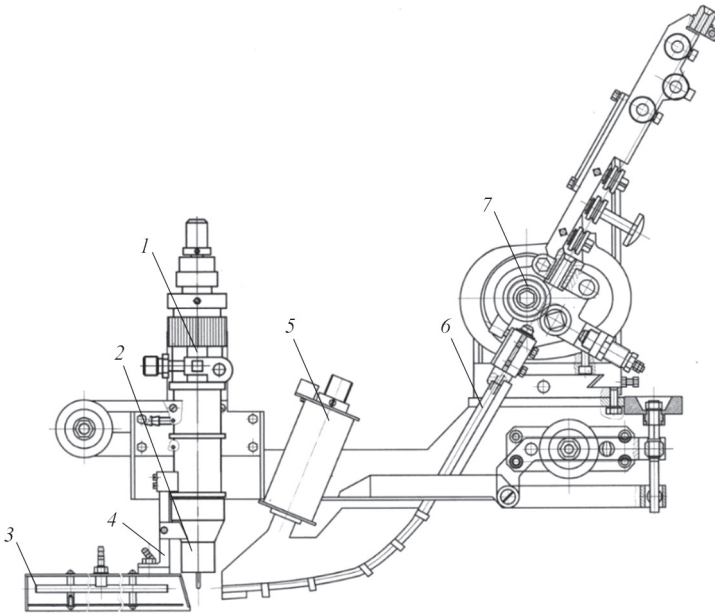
Конструктивна схема зварювальної головки для АДЗ: 1 — цанга із неплавким електродом; 2 — захисне сопло; 3 — захисний пристрій; 4 — система стеження захисного пристрою; 5 — електромагніт; 6 — направляюча для подачі присадного дроту; 7 — механізм подачі дроту
